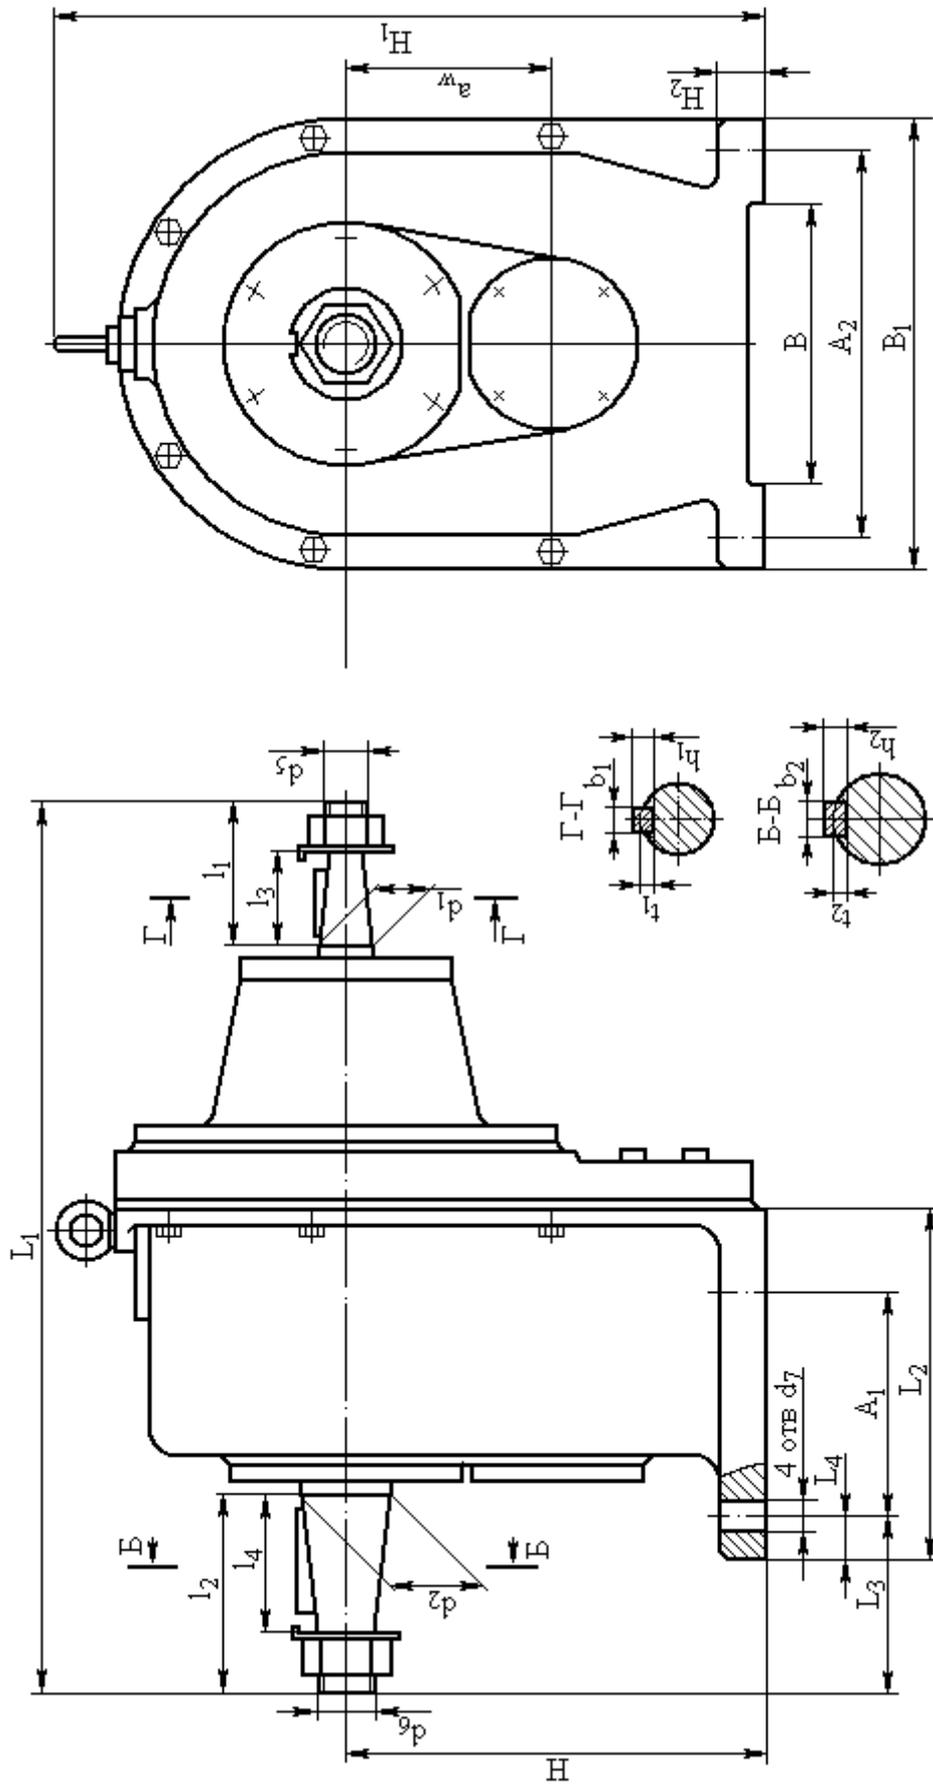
Цилиндрический двухступенчатый соосный редуктор типа Ц2С
